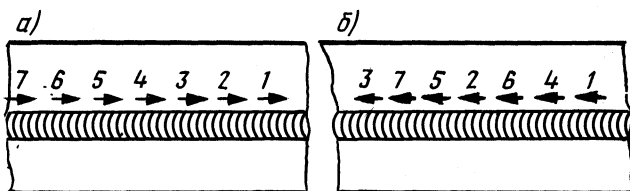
Сварка тонкого листового материала ступенями:
